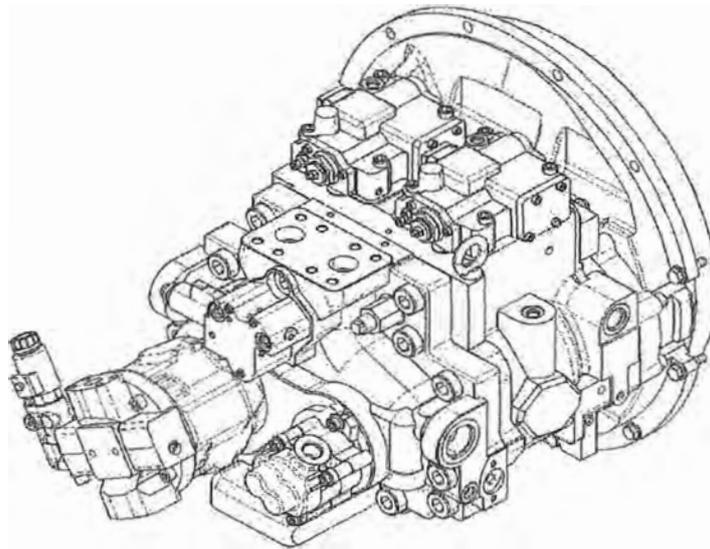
Vista Isométrica de la Bomba Hidráulica
